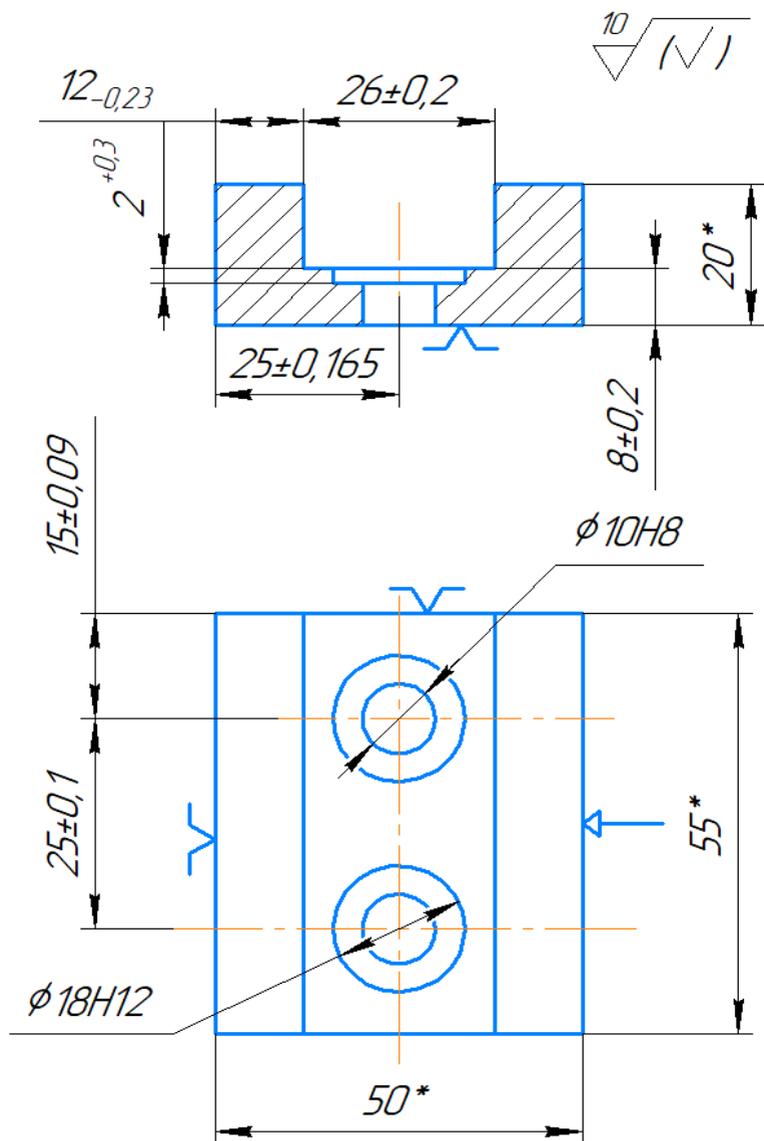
Эскизы заготовки из стали 20 и комплексной операции обработки детали «Планка» на станке модели 2254ВМФ4
